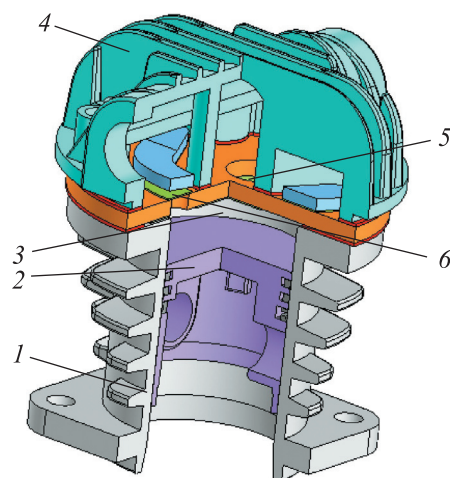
3D-модель ЦПГ опытного образца ПГЭМОД: 1 — цилиндр; 2 — поршень; 3 — РК; 4 — клапанная головка; 5 и 6 — всасывающий и нагнетательный клапаны
